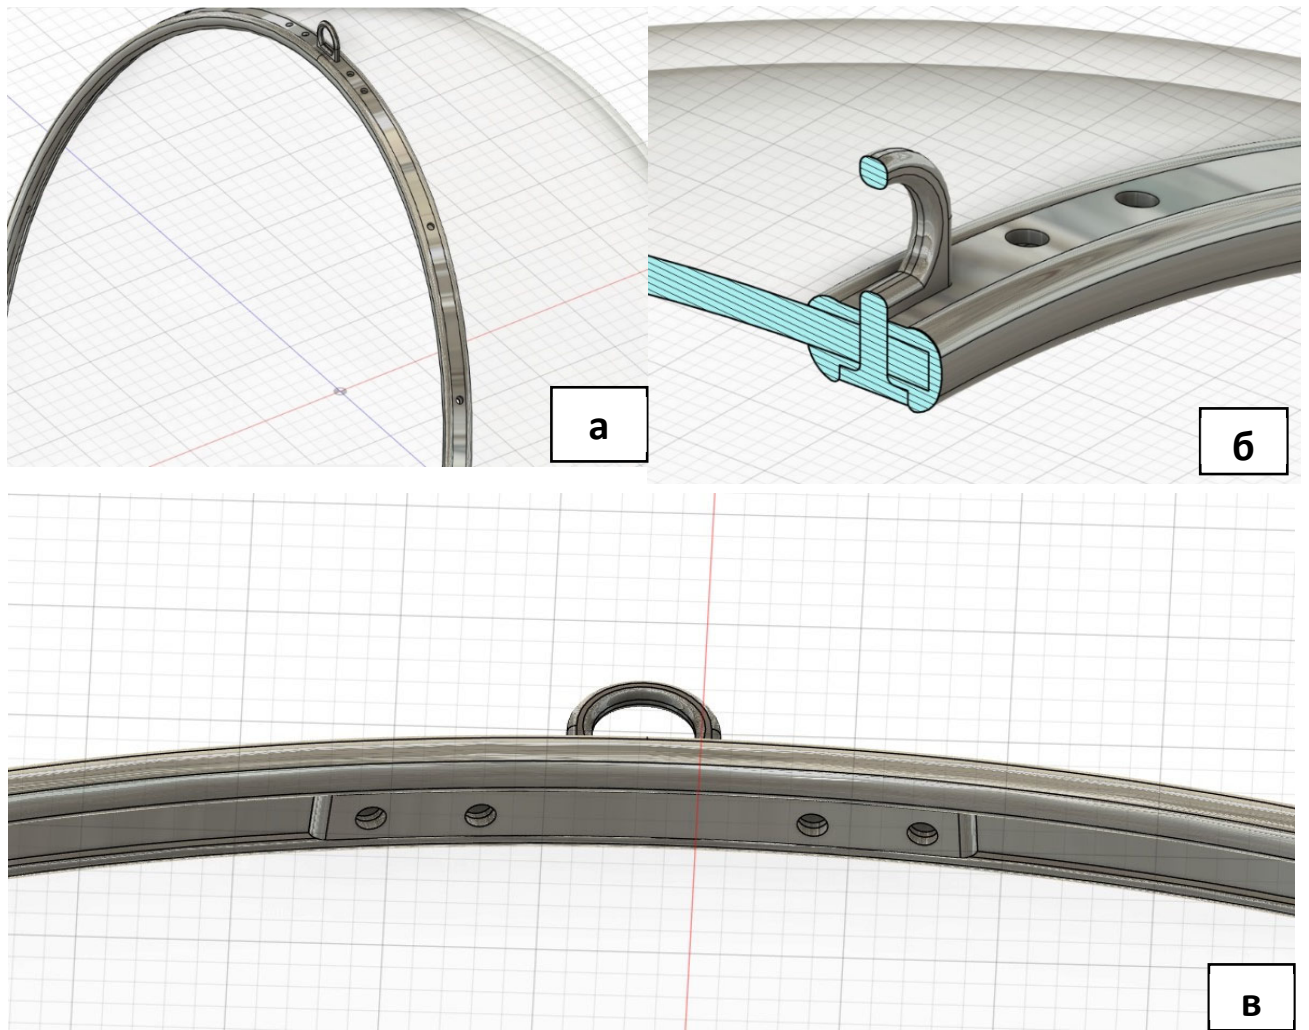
Сталевий обод і петля: а – загальний вигляд; б – вигляд у розрізі;
